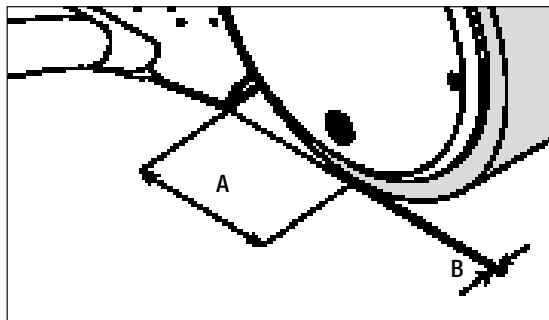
Plaque de serrage pour socle roulant de transport coulissant (17)
